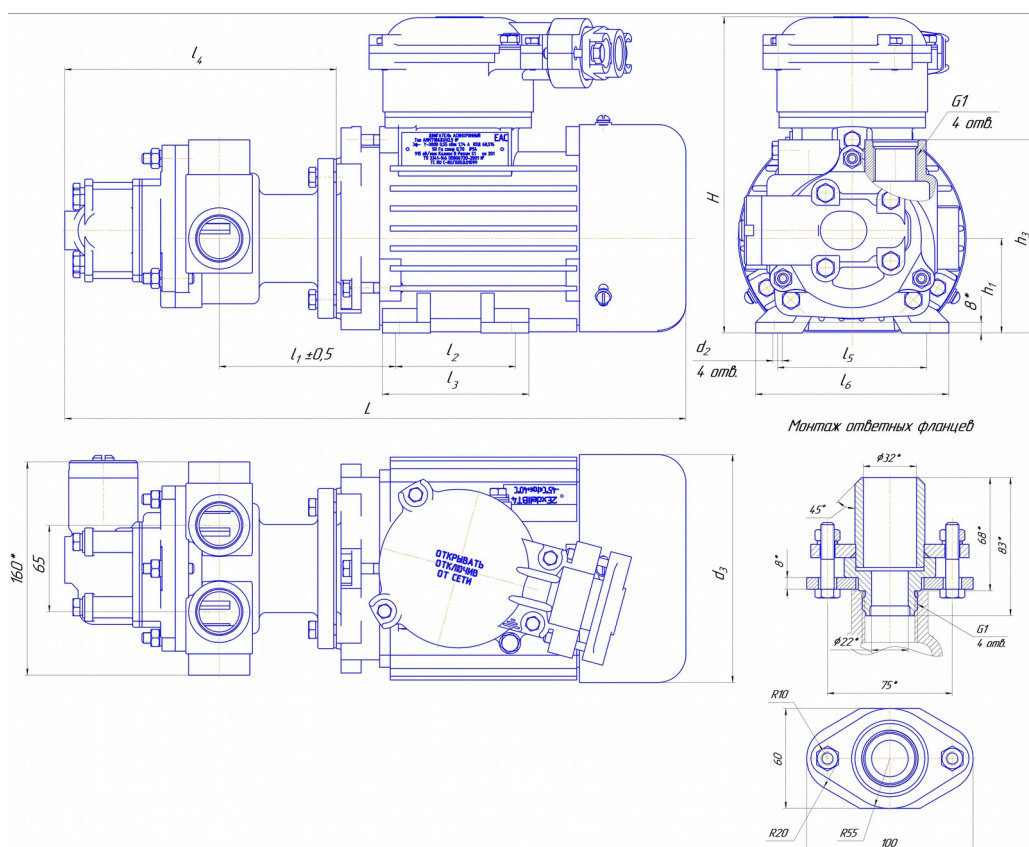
Габаритные и присоединительные размеры электронасосов БШМ-20, БШМ-40, БШМ-50, БШМ-70, БШМ-100 (на лапах), с осевым (линейным) и вертикальным расположением входного/ выходного патрубков корпуса.
